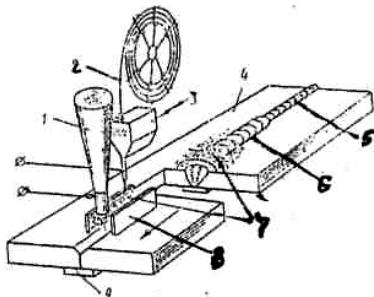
Автоматическая дуговая сварка под флюсом: 1 – бункер с флюсом; 2 – электродная проволока; 3 – сварочная головка; 4 – основной металл; 5 – сварочный шов; 6 – шлаковая корка; 7 – нерасплавленный флюс; 8 – ограничители флюса; 9 – медная пластина
